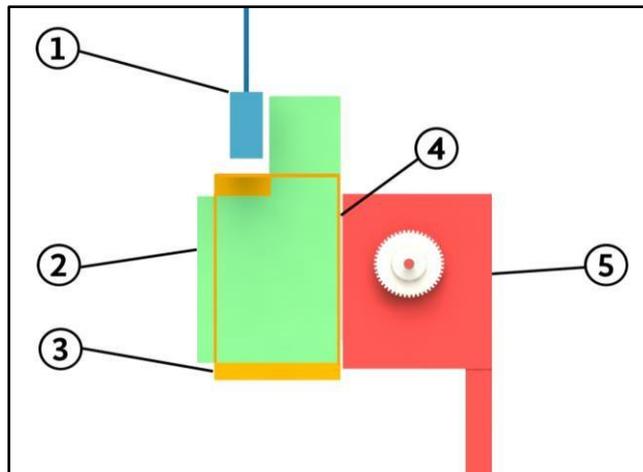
Ensamble de puerta enrollable: 1) Viga en el techo (obstáculo); 2) Dimensiones del abridor GH303 (volumen en verde); 3) Dimensiones del abridor actual GH101 (volumen naranja); 4) Bracket para montaje; 5) Placa de montaje de puerta enrollable
